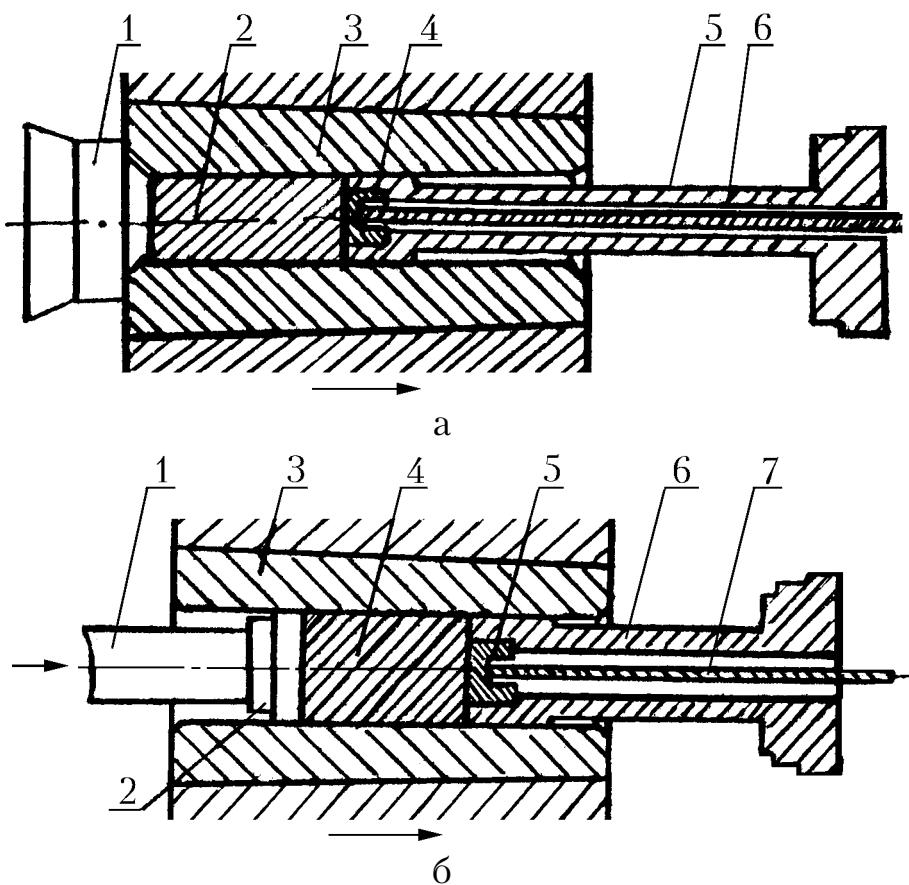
Схеми пресування профілю суцільного перерізу зі зворотним витіканням металу:
